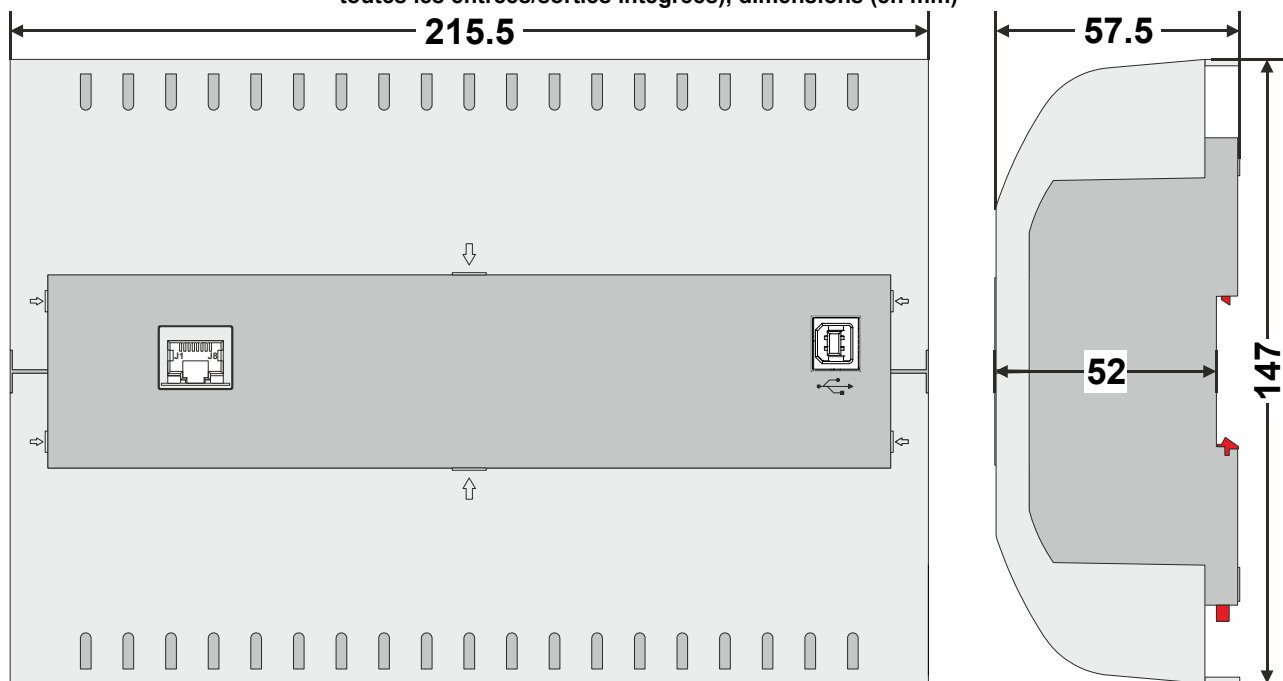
Régulateur EAGLEHAWK NX avec couvercles, dimensions (en mm)
